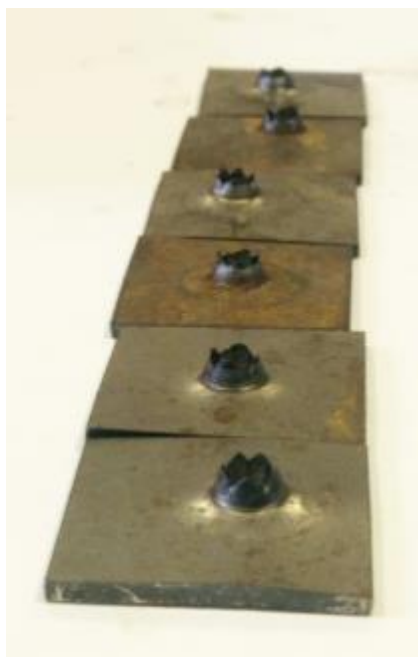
Тонколистовые заготовки с образованными в них отверстиями
